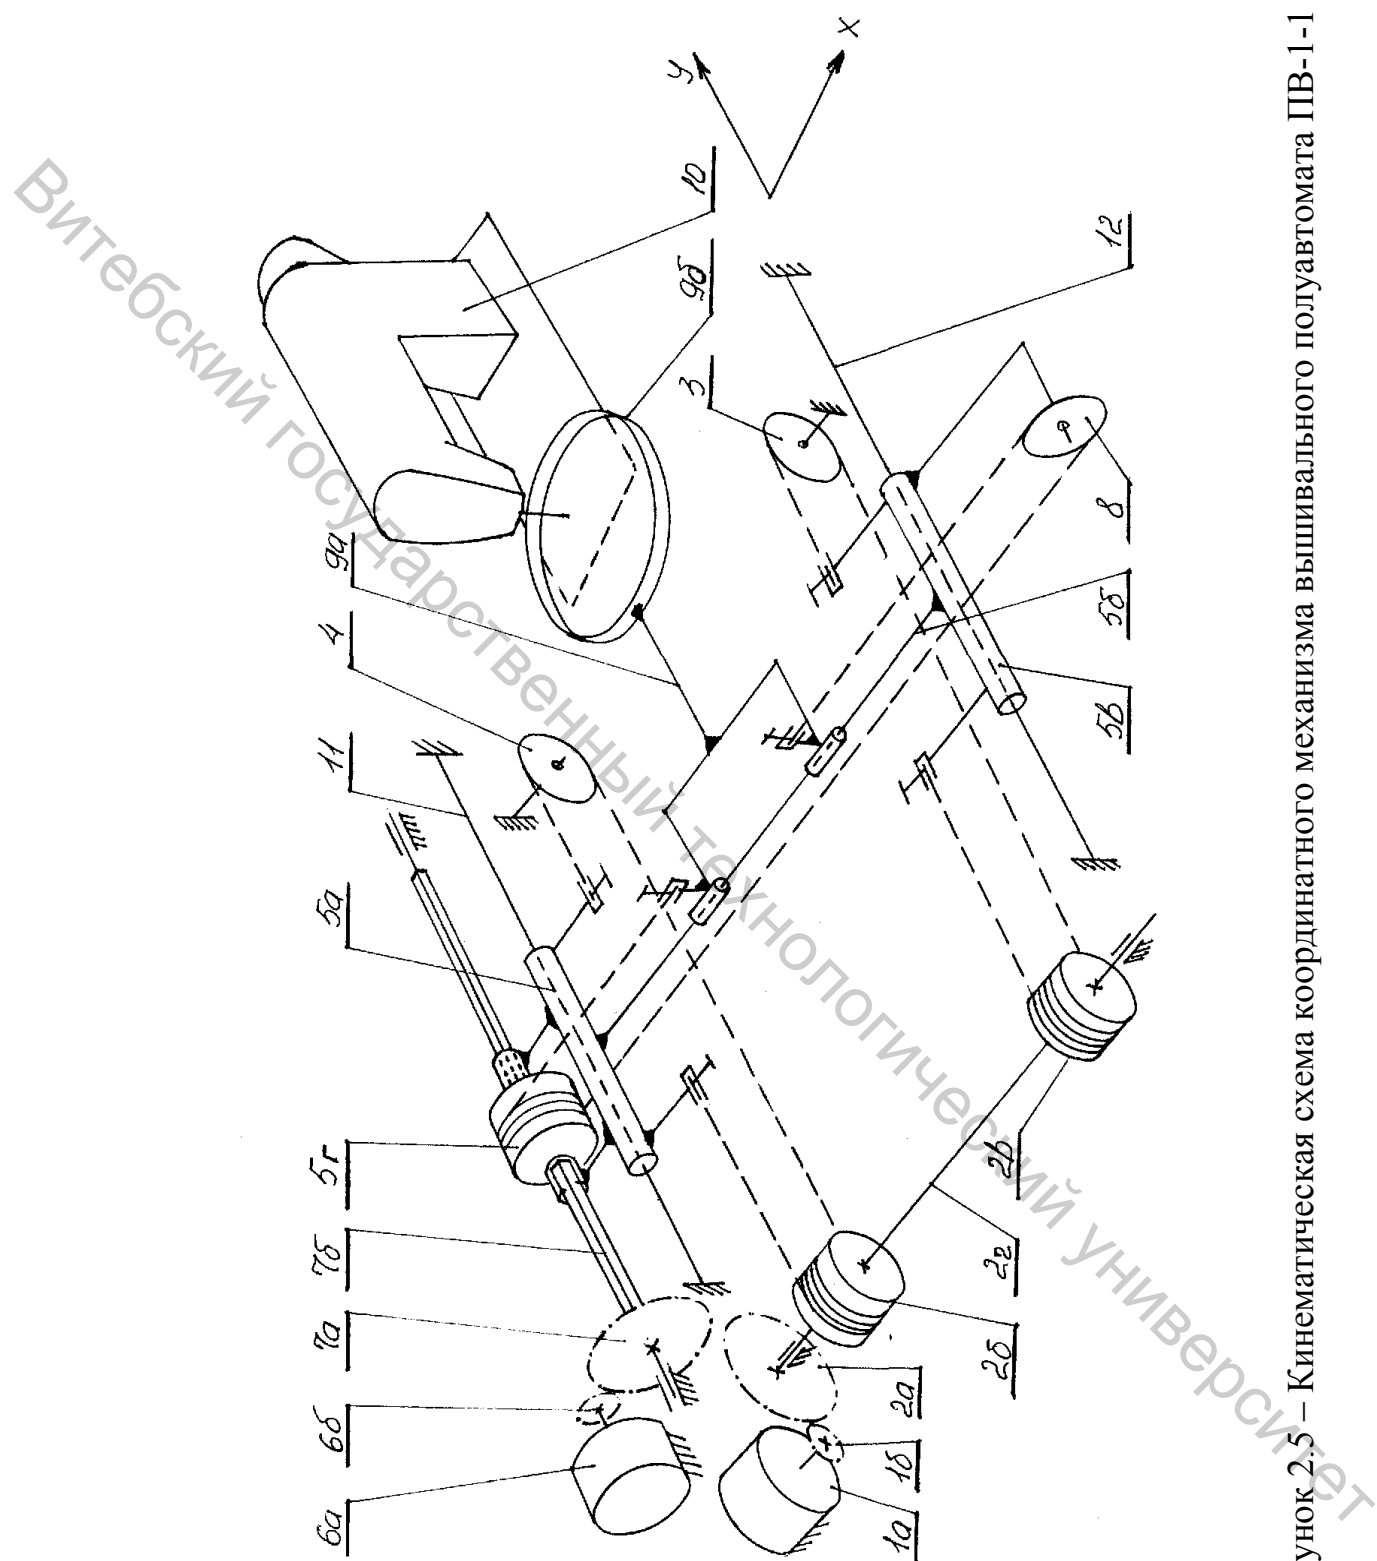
Кинематическая схема координатного механизма вышивального полуавтомата ПВ-1-1
